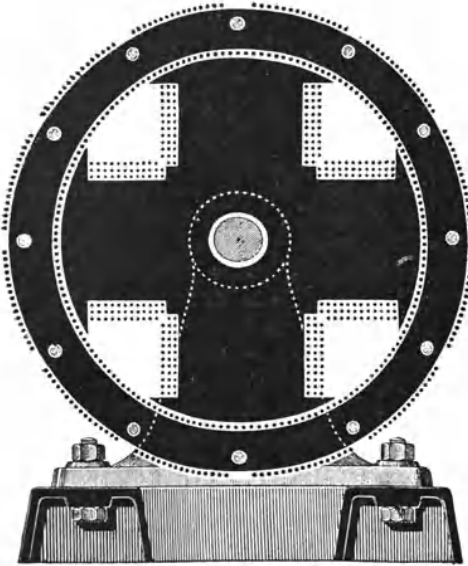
Schema der Siemens'schen Innenpol-Maschine.
